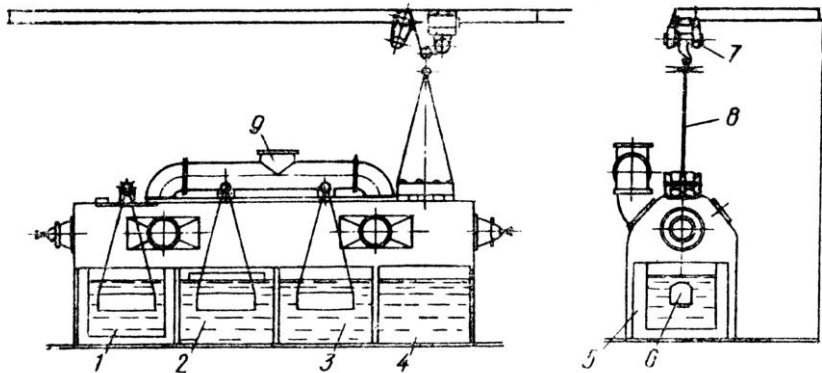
Установка проходного типу для очищення деталей у розплаві солей: 1 – соляна ванна; 2 – ванна для проточної води; 3 – ванна для кислотного розчину; 4 – ванна для гарячої води; 5 – кожух установки; 6 – сортовик для деталей; 7 – монорейка з тельфером; 8 – підвіска; 9 – відсмоктувач повітря
